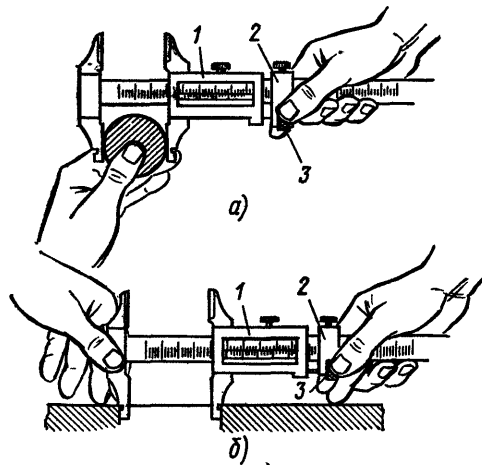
Приемы измерений штангенциркулем ШЦ-II
